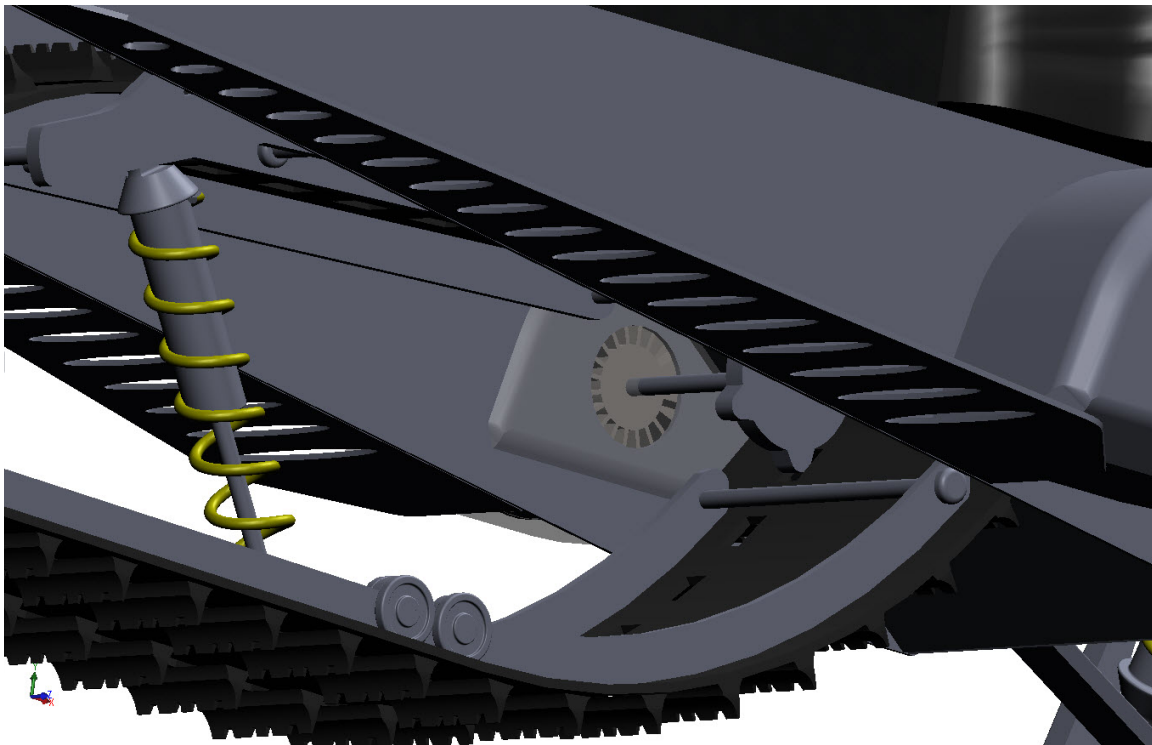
Gjennomsiktig motorkasse viser motorplassering ved direkte drift. Dempersystem vist fra baksiden.
